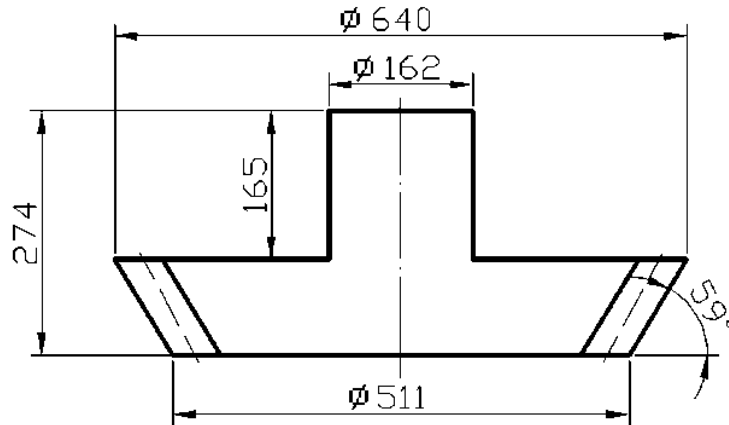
Креслення готової деталі «диск-шестерня конічна»
